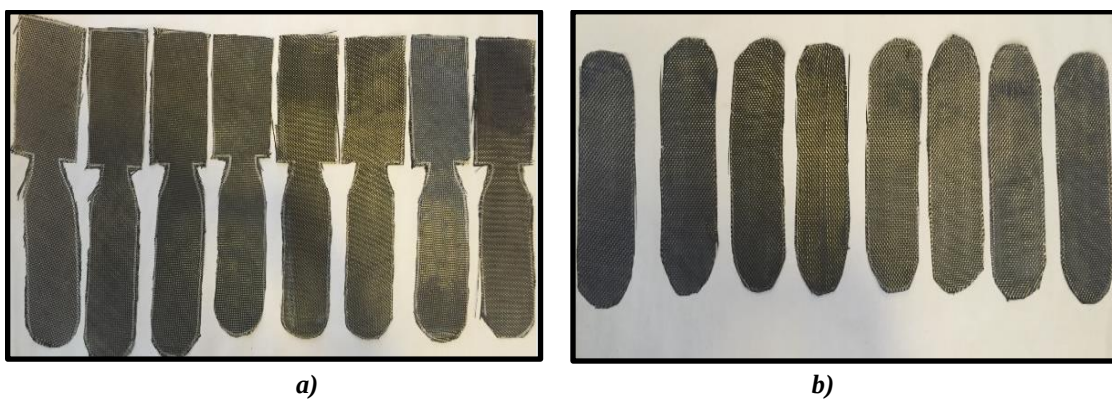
Corte de fibra: a) Pieza superior; b) Pieza inferior.
